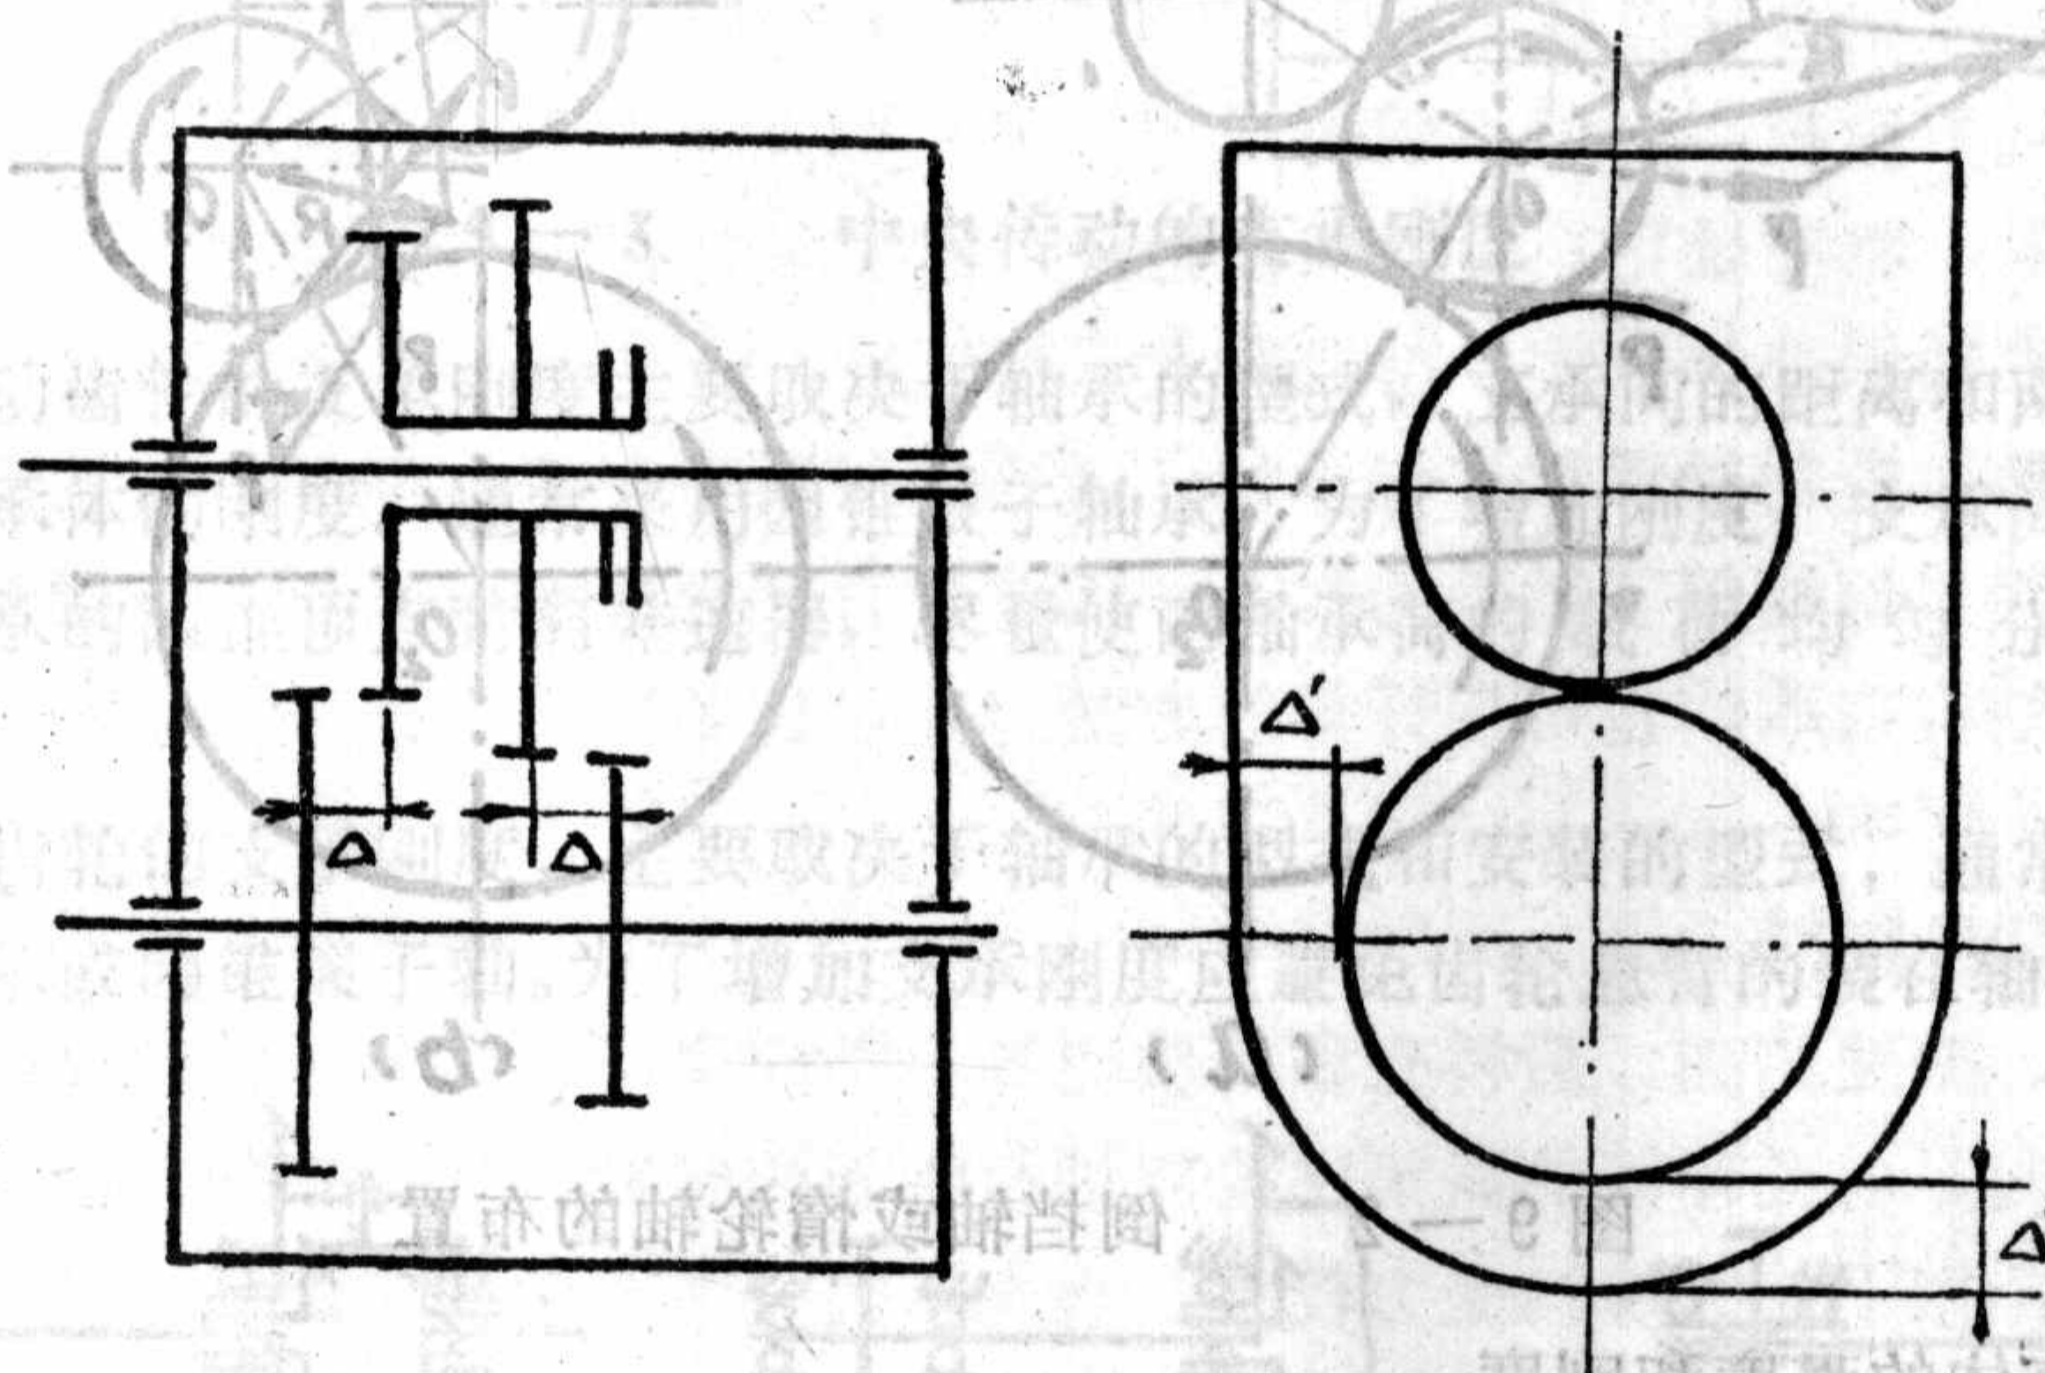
1 齿轮和齿轮间（轴向）、齿轮和箱壁间的间隙
